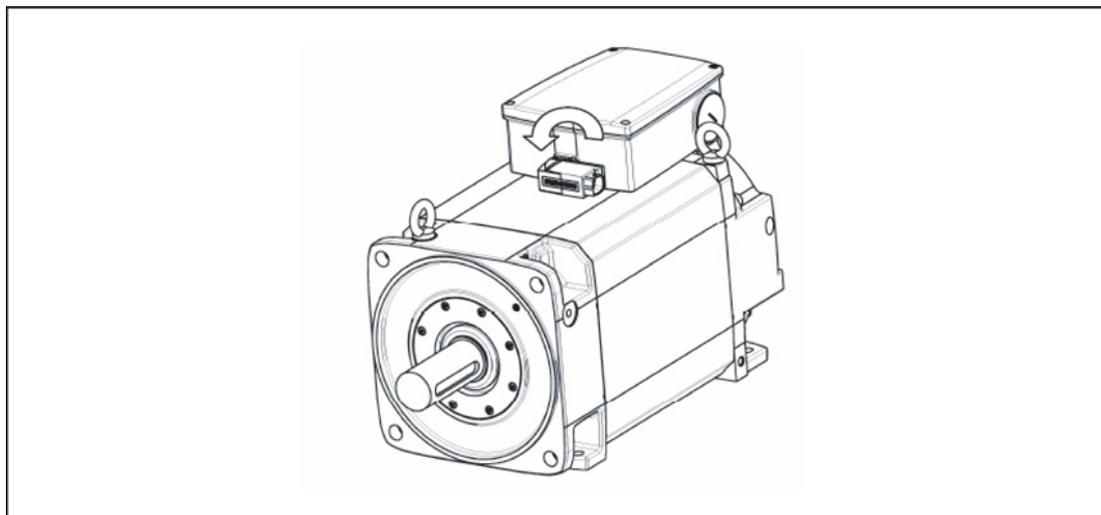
Motor mit DRIVE-CLiQ Schnittstelle (Beispiel)
